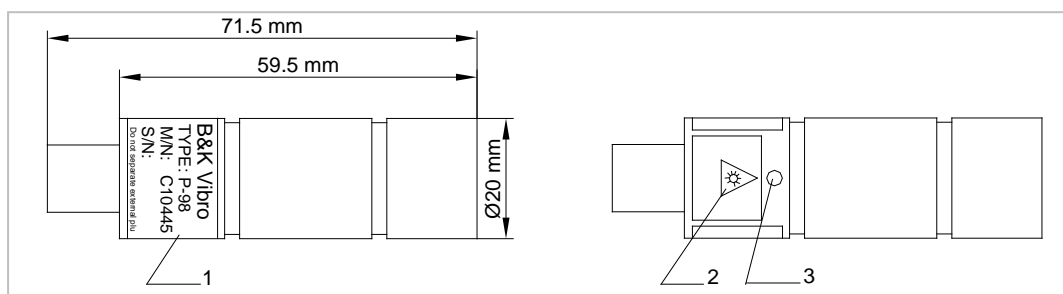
Bemaßung Sensor / Dimensioning Sensor / Dimensionement Capteur
